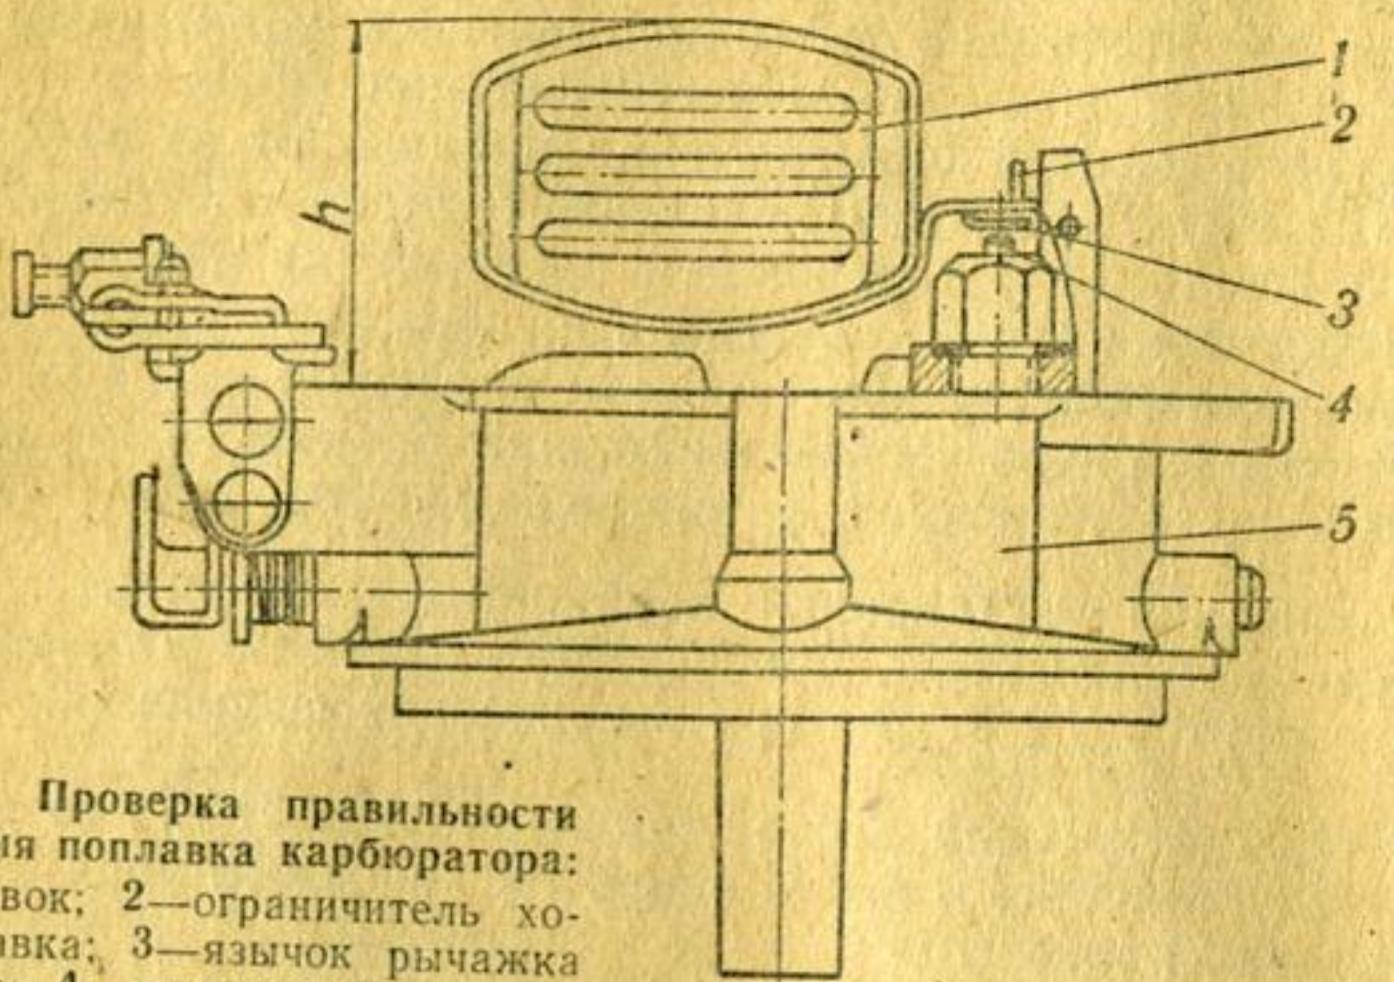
Проверка правильности положения поплавка карбюратора:
